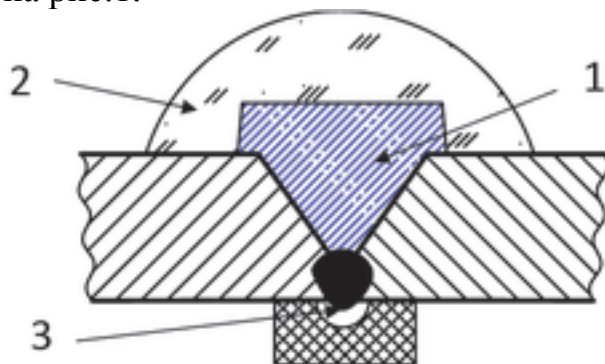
Схема сварки с термитным наполнителем:
